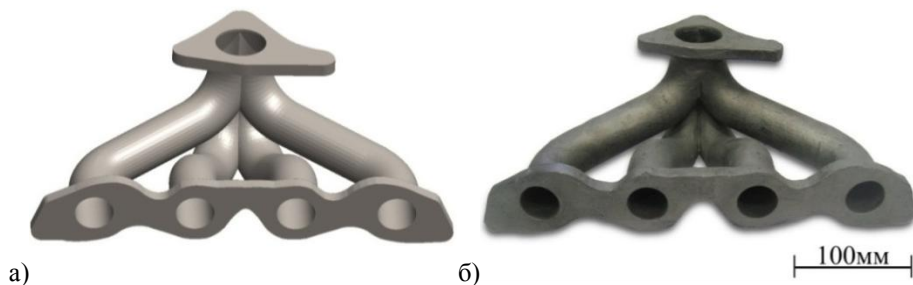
Коллектор выпускной: трехмерная модель отливки (а) и отливка (б)
